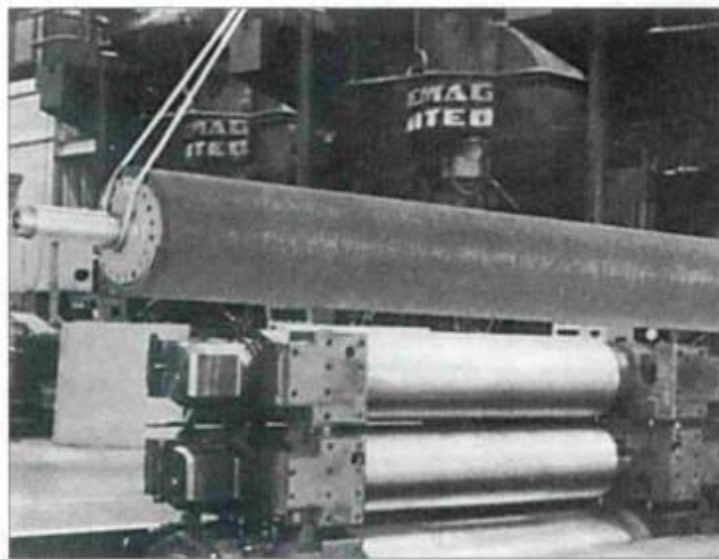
Escova cilíndrica para aplicação em laminadores
